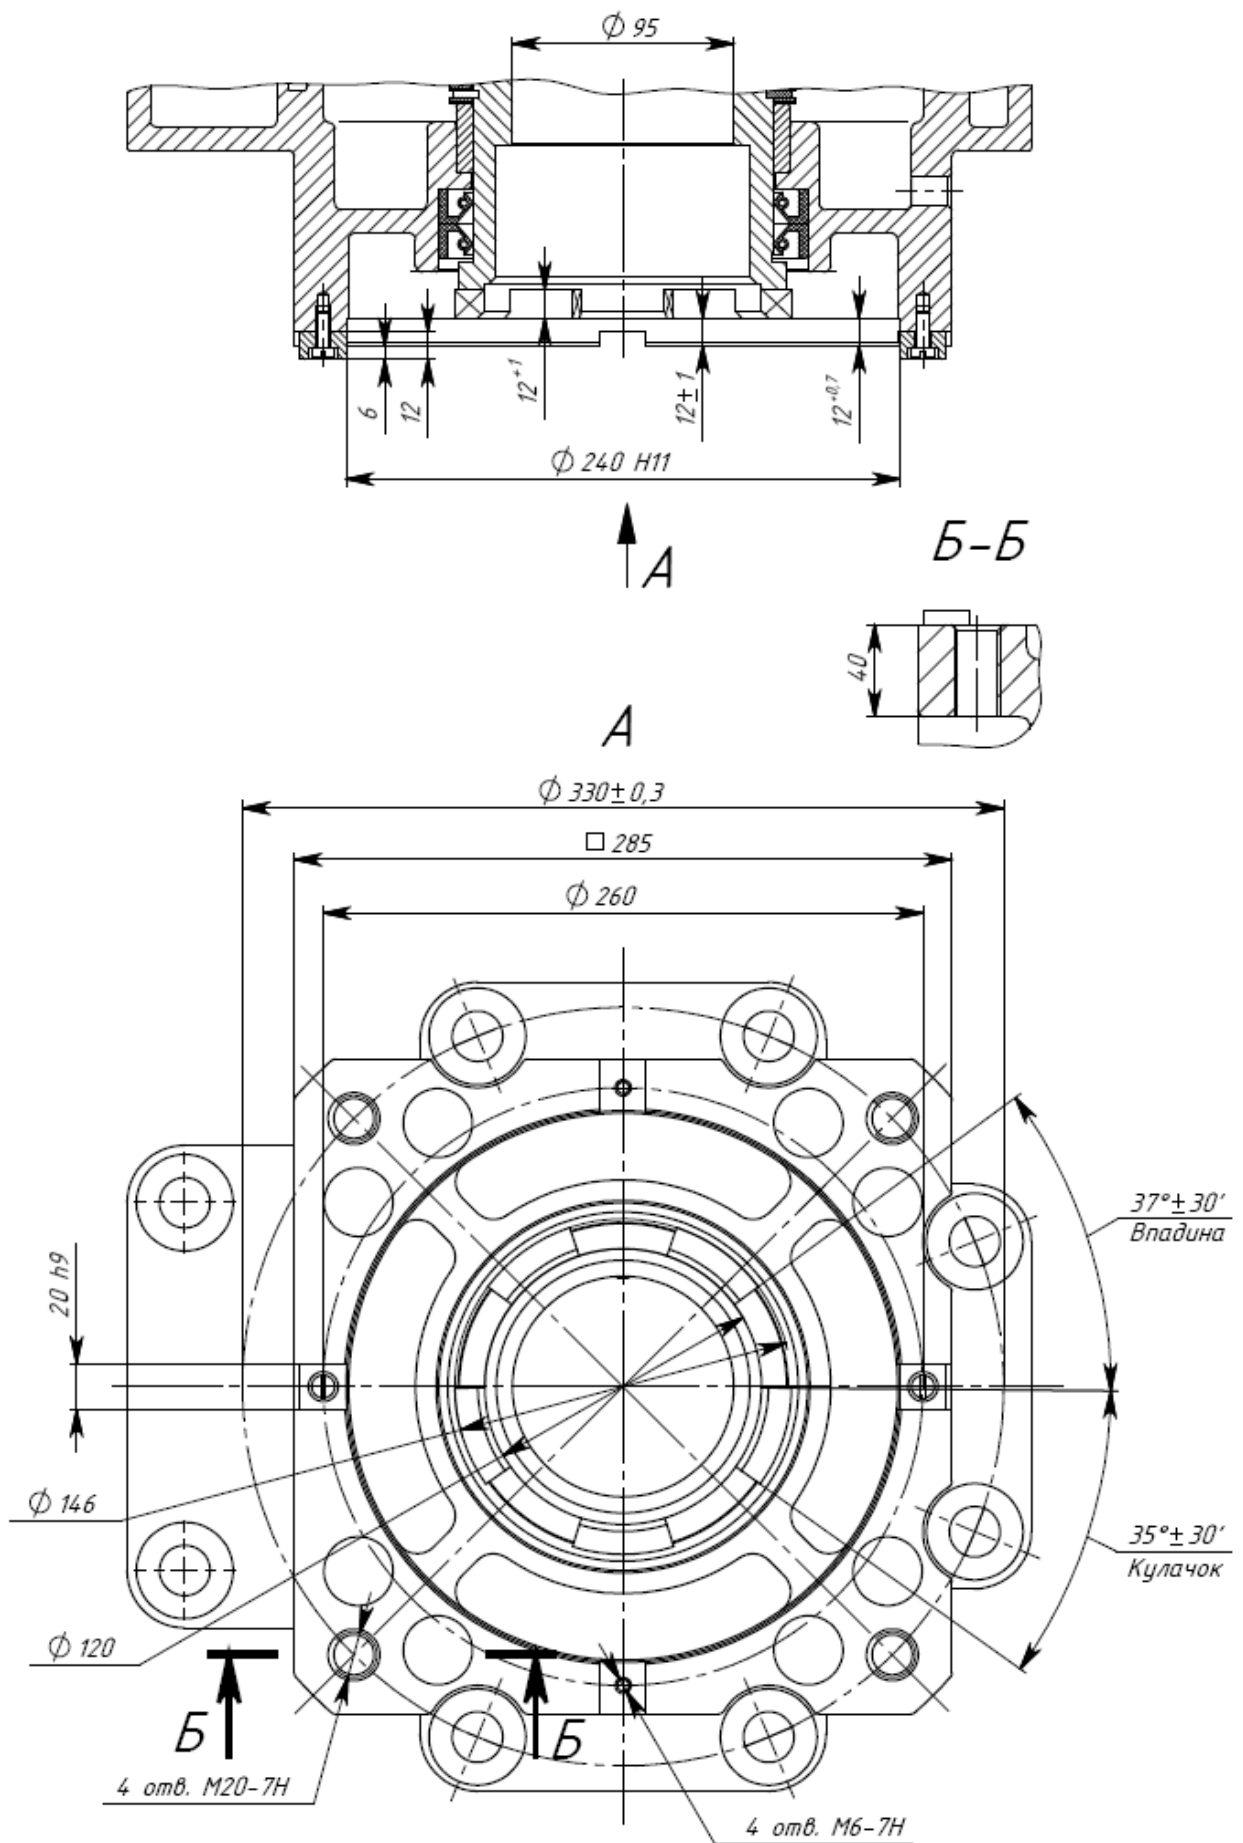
Присоединение типа Г для конструктивной схемы 43
